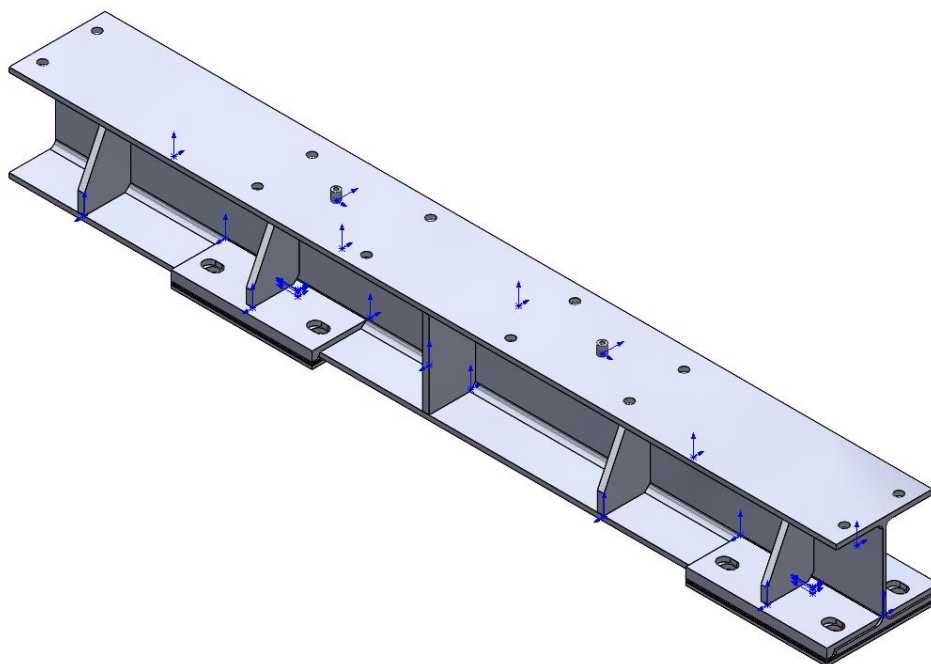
Балка (4А.0003.000 СБ) в сборе, изометрический вид
